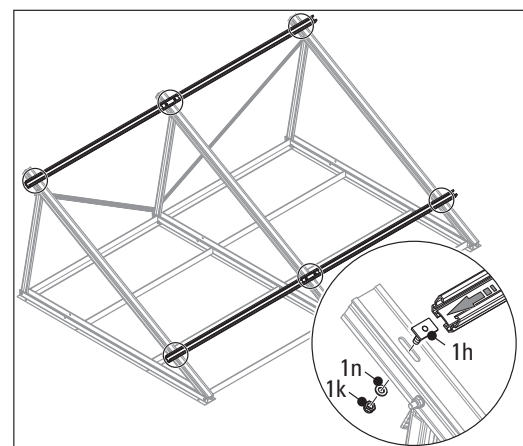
Montar las guías de perfil de montaje, 2º paso
